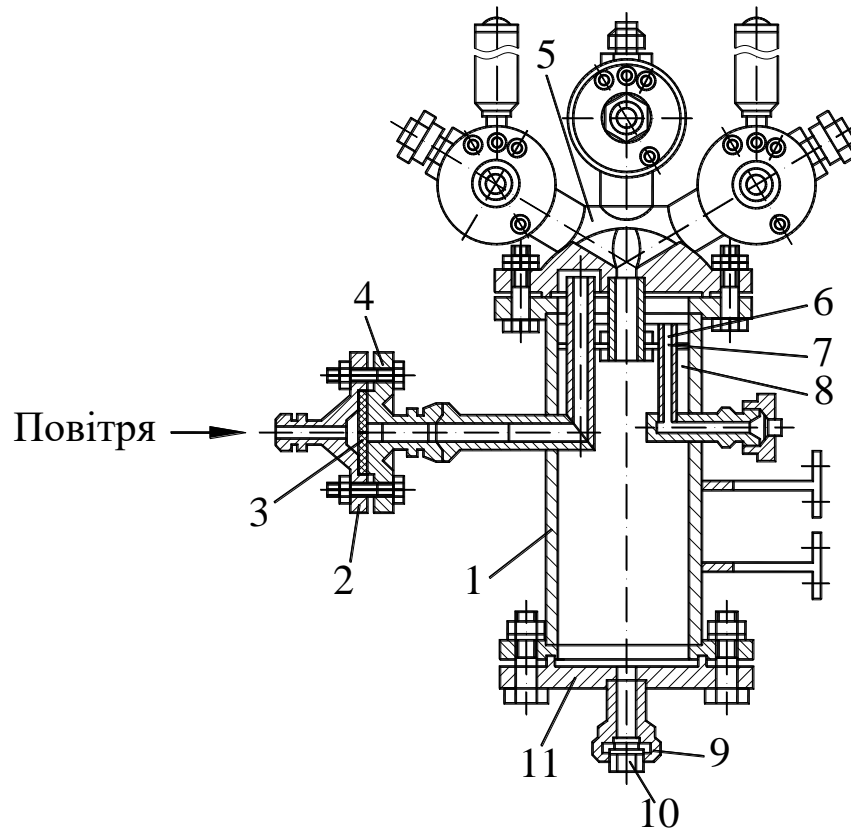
Прилад постійного тиску установки: 1 – корпус фільтра; 2 – кришка клапана; 3 – мембрана; 4 – корпус клапана; 5 – блок випробувальних камер; 6 – зливний патрубок; 7 – механічний дисковий фільтр; 8 – вода; 9 – гайка; 10 – заглушка; 11 – кришка фільтра.
